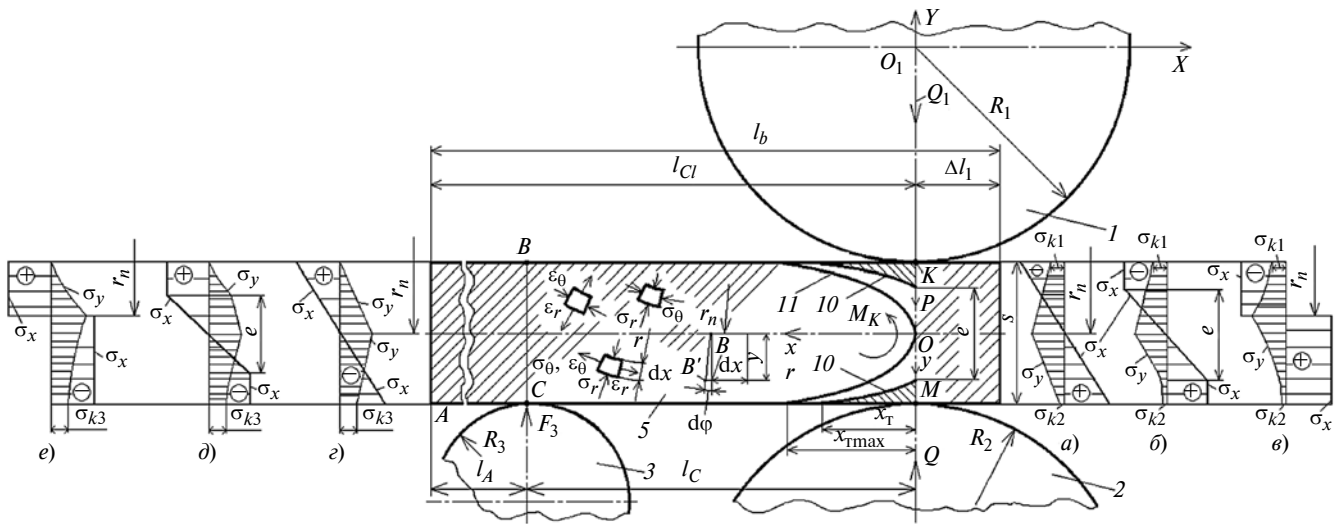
Расчетная схема формы и размеров очага деформаций в начале подгибки кромки заготовки: 1 и 2 — верхний и нижний валки; 3 — боковой валок; 5 — заготовка
